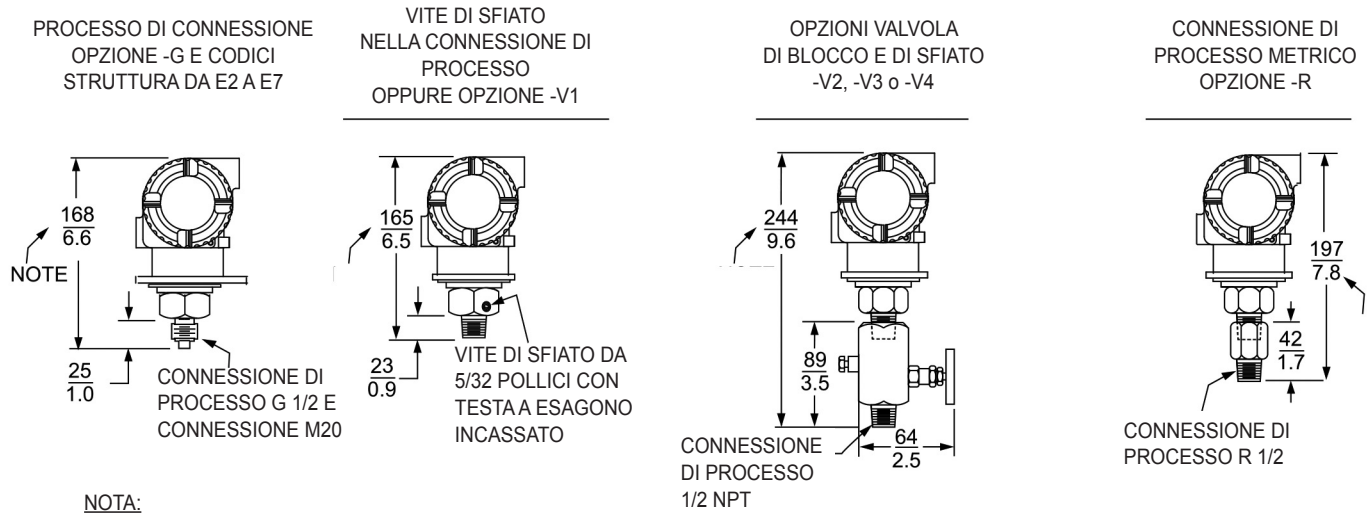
Trasmettitori a collegamento diretto AP/GP
